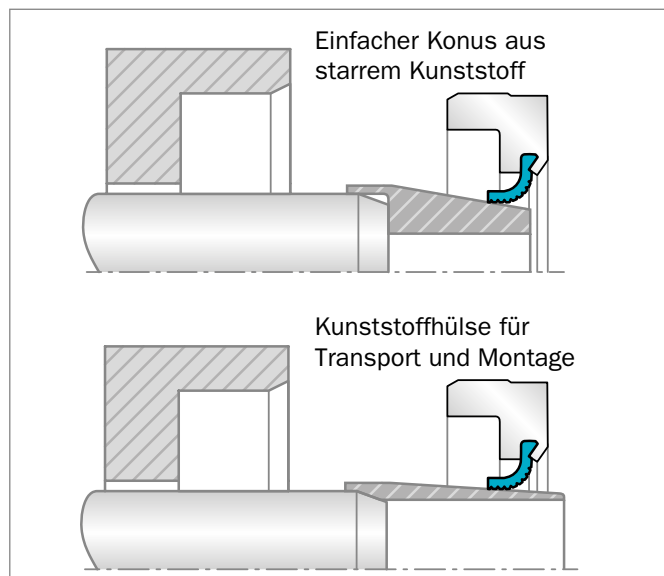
Montagewerkzeuge für den Einbau auf Wellen
